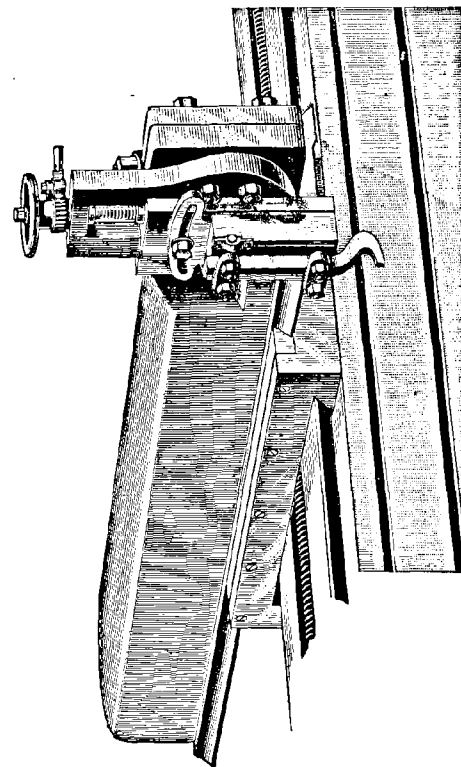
Disposition de la tête pour utiliser la machine comme raboteuse latérale.
